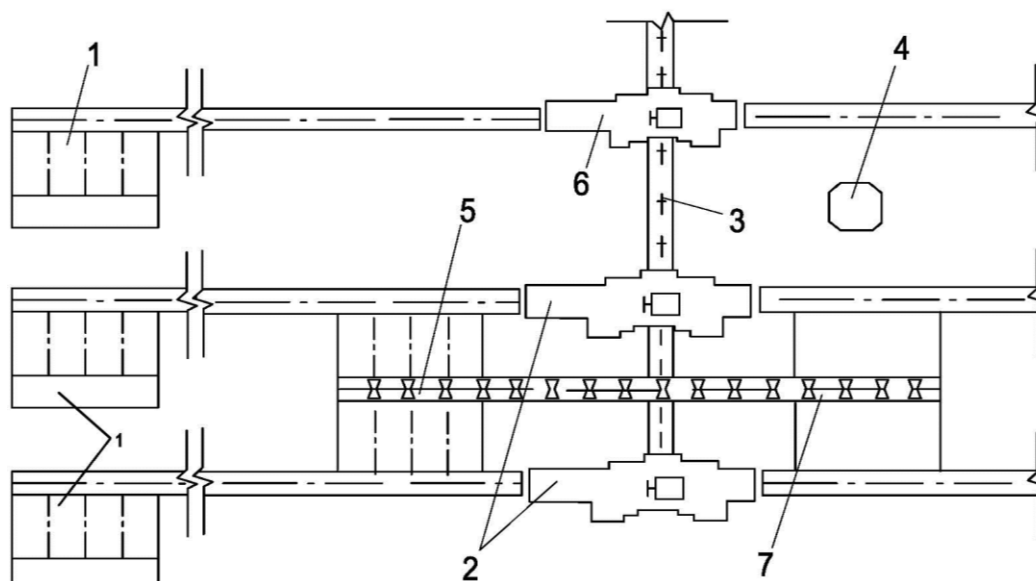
Технологическая схема окорки пиловочника с параллельной установкой станков [1]: 1 – питатель; 2 – станок окорочный ОК40-2; 3 – транспортер для коры; 4 – кабина оператора; 5 – сбрасыватель бревен двухсторонний; 6 – станок окорочный ОК63-2; 7 – рольганг возврата бревен
